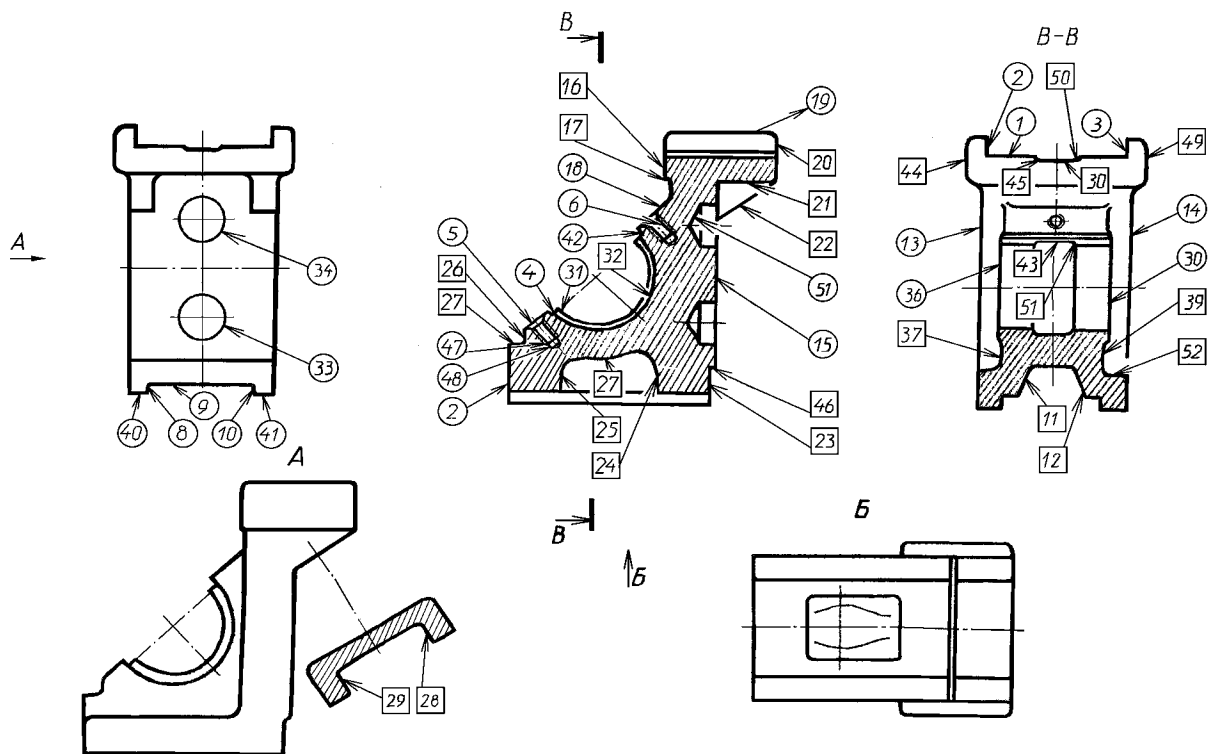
Чертеж корпуса с пронумерованными поверхностями
